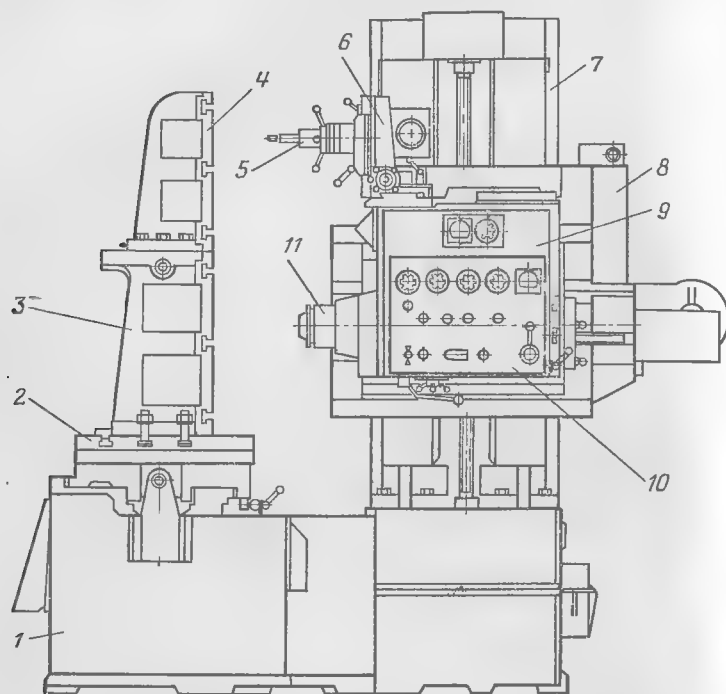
Копировально-фрезерный станок модели 644Б.
